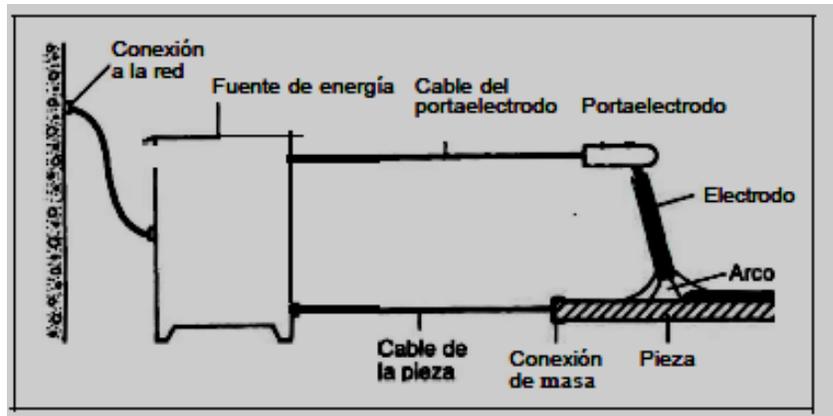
Equipo de soldadura de arco con electrodo revestido
